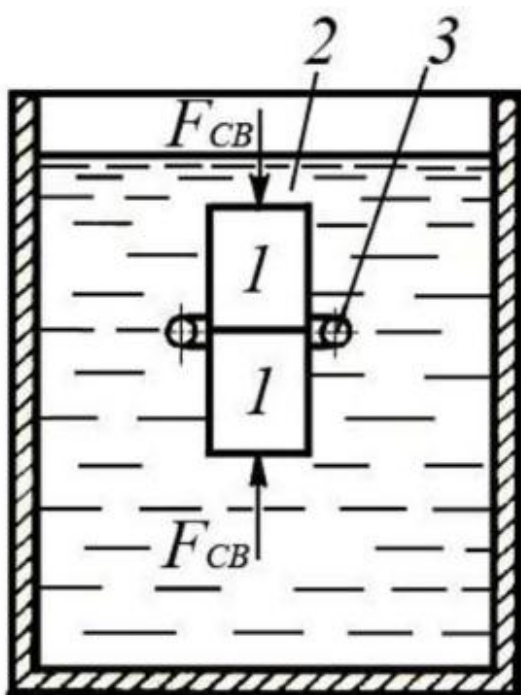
Схема дифузійного зварювання в рідкому середовищі: 1- деталі, що зварюються; 2 – рідке середовище; 3 - індуктор
